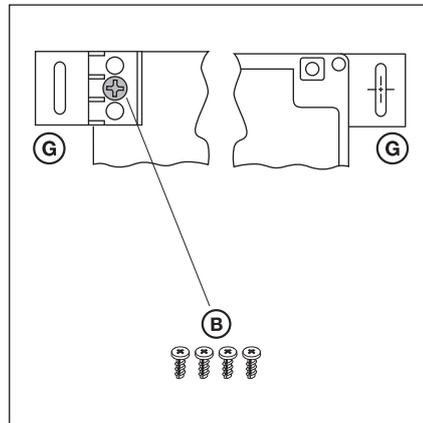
Befestigung der Montagefüße, Ansicht von hinten und vorne
